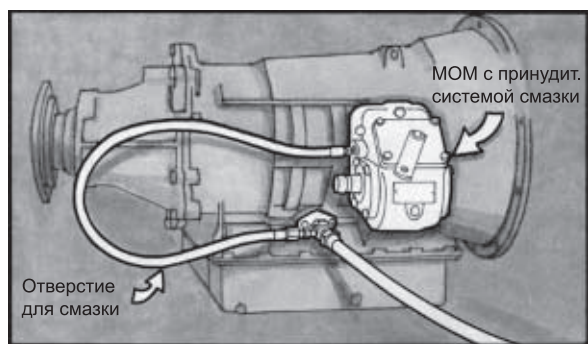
Если MOM прикрепляется к автоматической коробке передач, шланг для подачи смазки должен быть подсоединен к шлангу охлаждения смазки коробки передач
